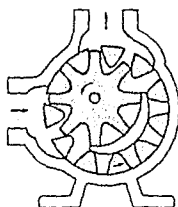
BOMBA DE ENGRANE INTERNO.
